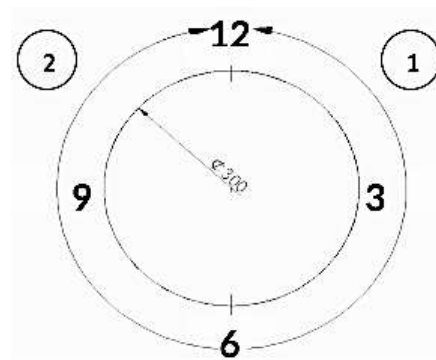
Схема сварки корневого шва в положении PF/5G (на подъем) в два этапа из положения «6» против часовой стрелки и по часовой стрелке
